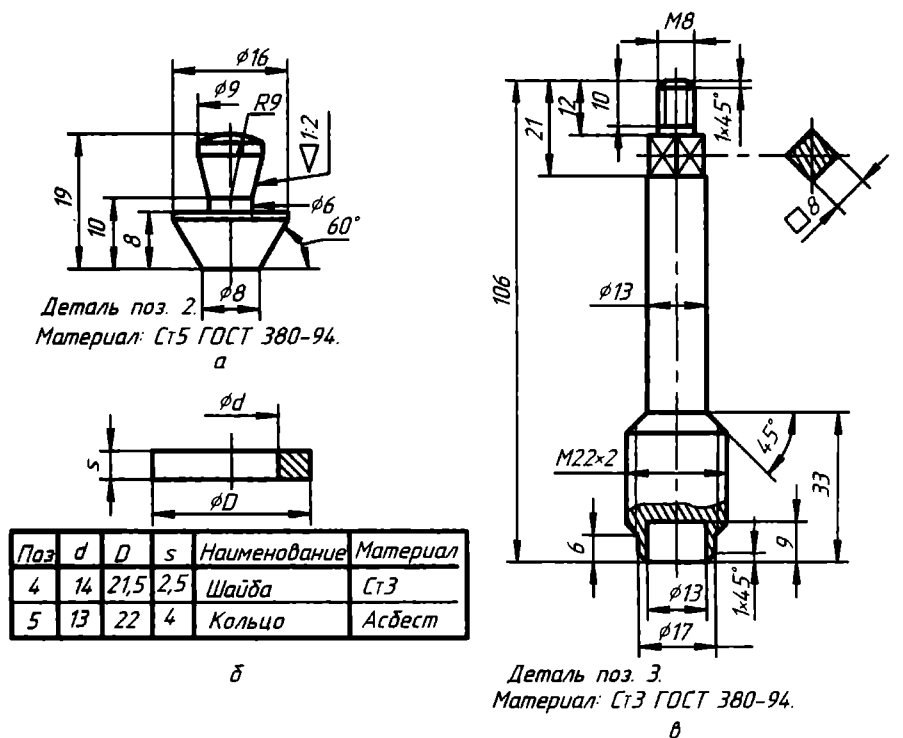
Чертежи: а — клапана; б — опорной шайбы, сальникового кольца; в — шпинделя
